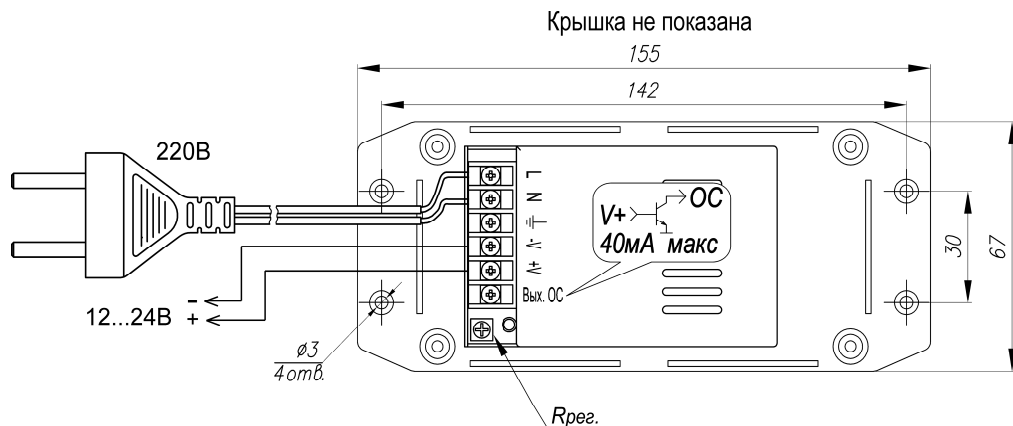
Устройство, габаритные и установочные размеры, подключение БП-18Вт
